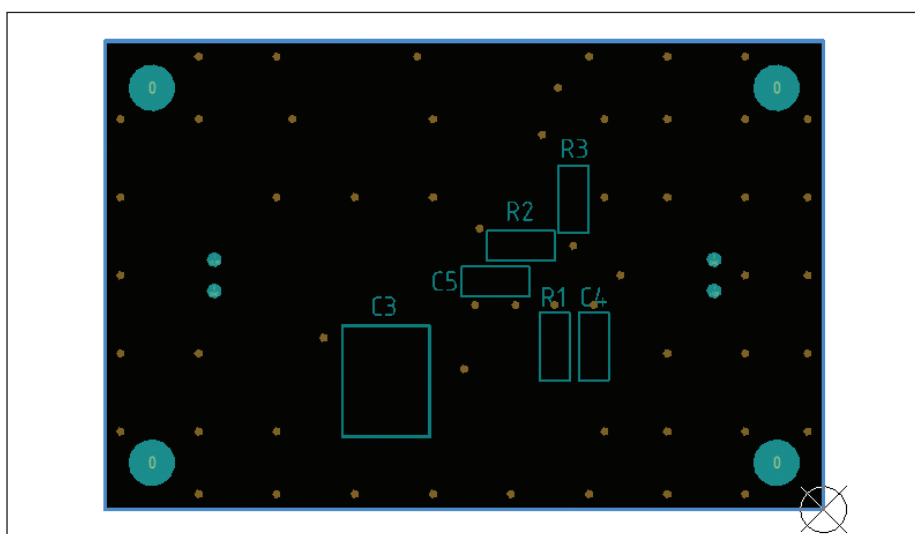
Сформированный в Altium Designer вид снизу сборочного чертежа
